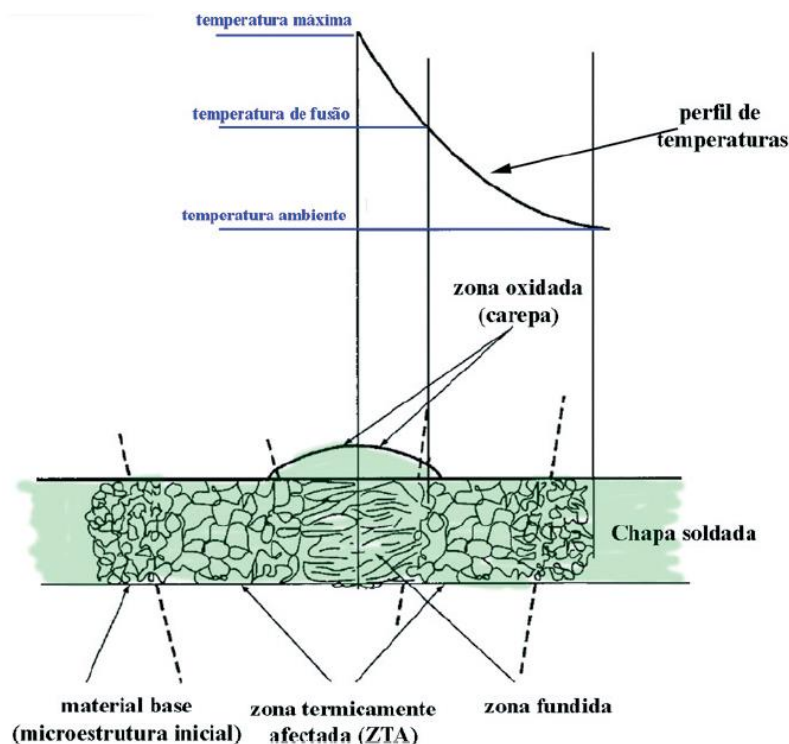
Esquema de um cordão de soldadura em corte transversal onde se apresenta a zona fundida (ZF), a zona termicamente afetada (ZTA) e o material base (MB) [35]
